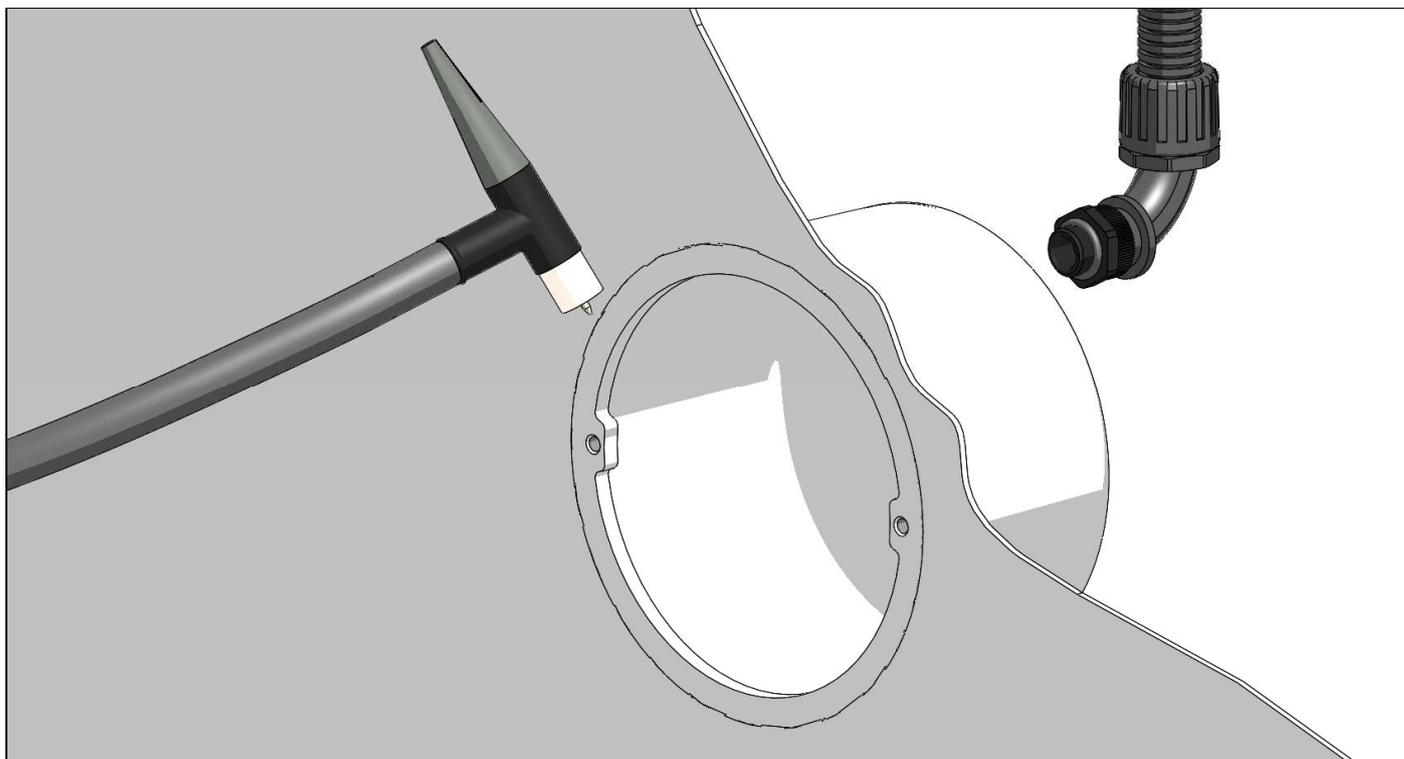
Boîtier à sceller bassin en inox – soudage à fleur avec le bassin (procéder ensuite au montage étanche du système de protection des câbles)
